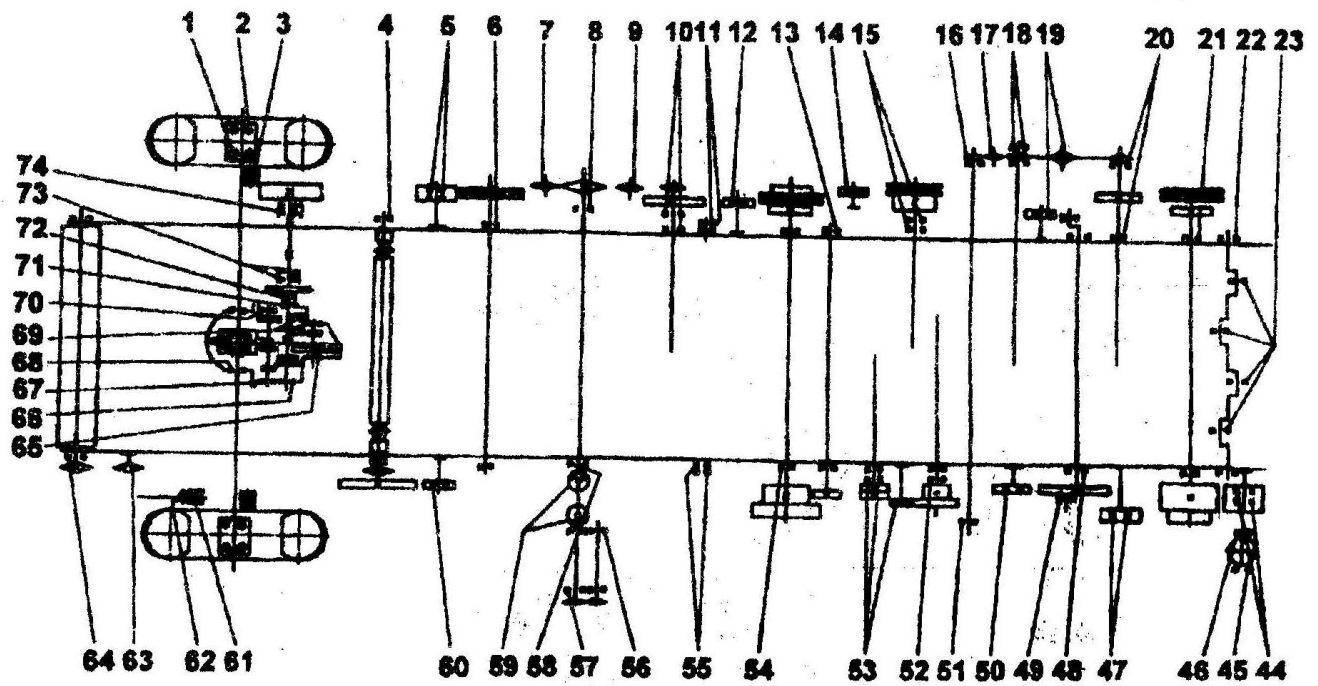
Схема расположения подшипников качения комбайна КЗС-3 (без жатки)
